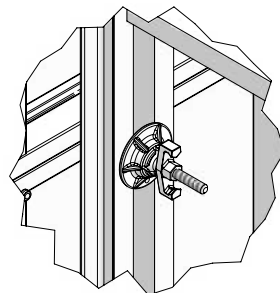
Detail – Halteschraube auf Stützbockseite
